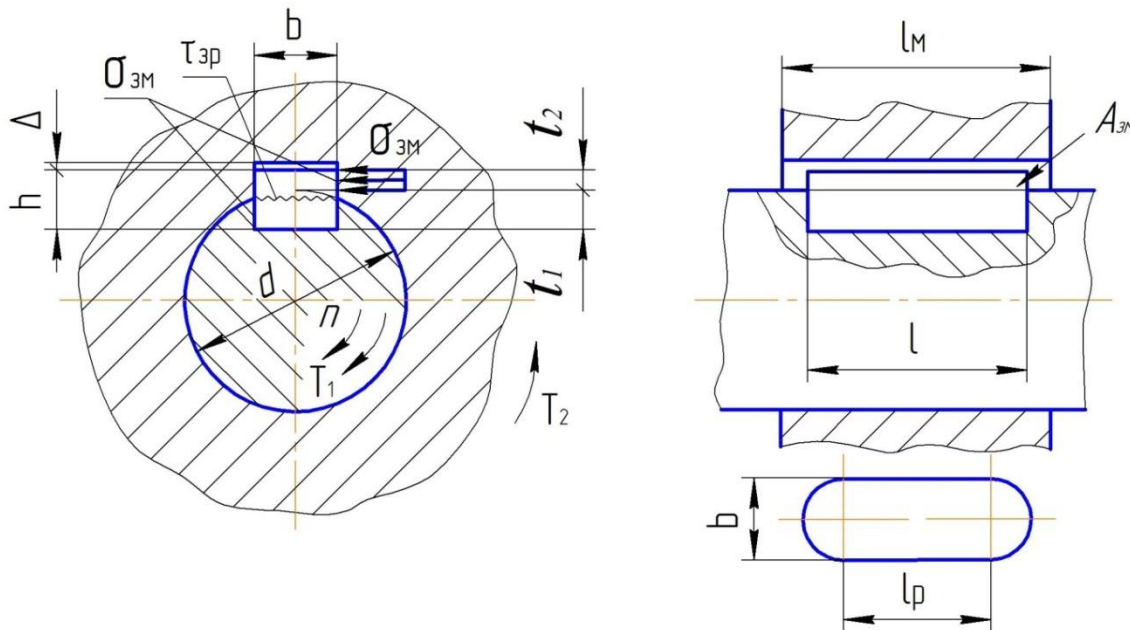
Конструкція шпонкового з'єднання з призматичною шпонкою
